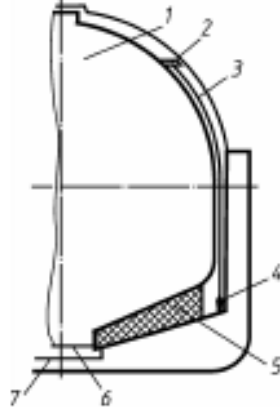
Опора сфероциліндричного танка:
